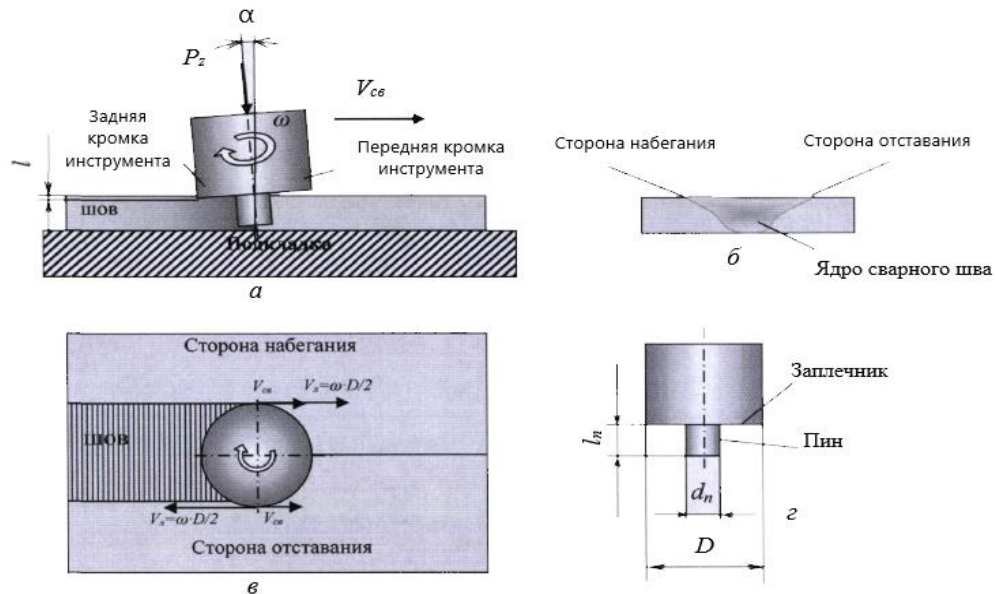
Сущность сварки трением с перемешиванием:
